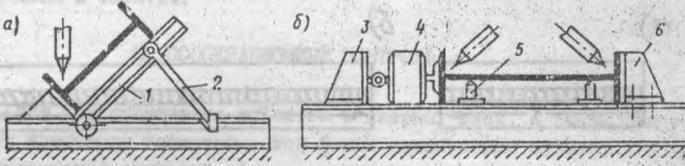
Приспособления для сварки двутавровых балок; а-стеллаж с подставкой; б-кондуктор с пневматическим прижимом; 1-откидной упор; 2-стойка; 3-неподвижный упор; 4-пневматический прижим; 5-подставка для стенки балки; 6-передвижной упор.
